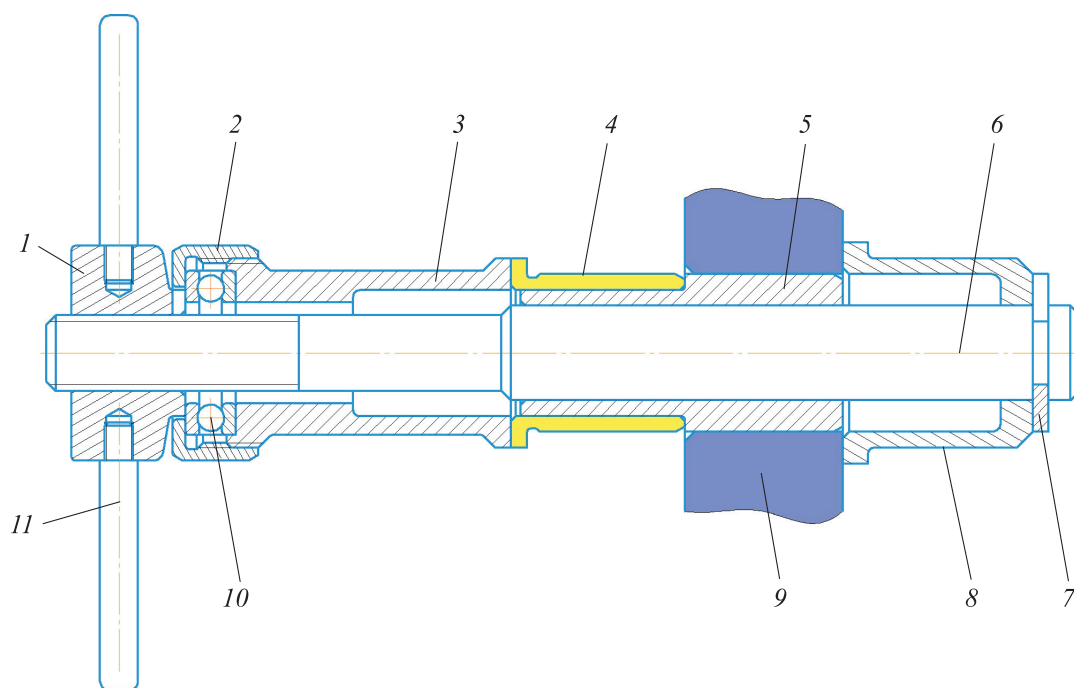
Конструктивная схема приспособления с ручным винтовым приводом для запрессовки втулки в отверстие корпусной детали
